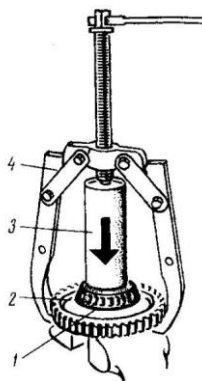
Напрессовка внутренней обоймы конического подшипника на вторичный вал: 1 - внутренняя обойма подшипника; 2 = вторичный вал; 3 - наставка; 4 - съемник
